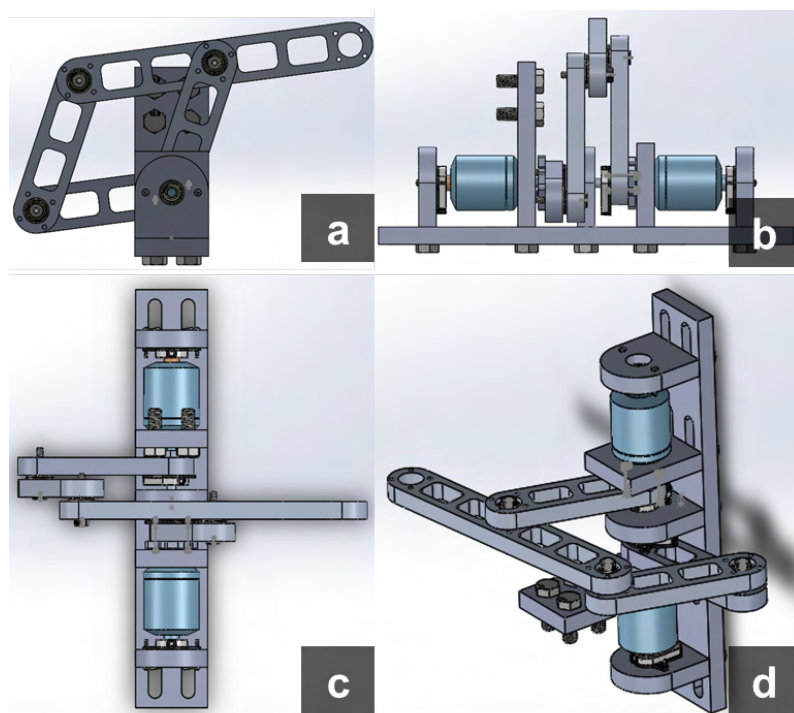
Vistas da montagem de um braço com SEA. a) Vista Superior. b) Vista lateral. c) Vista frontal. d) Vista isométrica.
